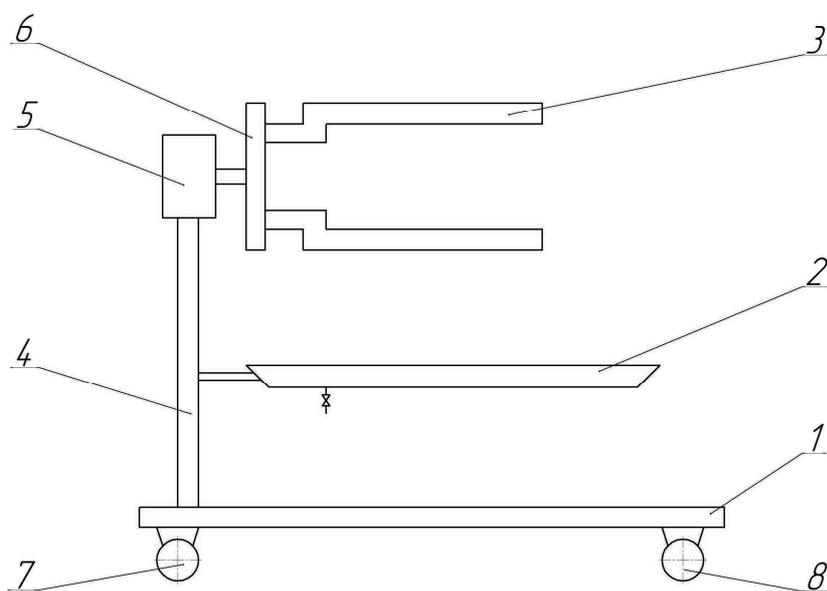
Общая схема стенда для ремонта ДВС: 1 – тележка; 2 – поддон; 3 – кронштейн; 4 – рама; 5 – устройство поворотное; 6 – план-шайба; 7 – колесо; 8 – колесо поворотное
